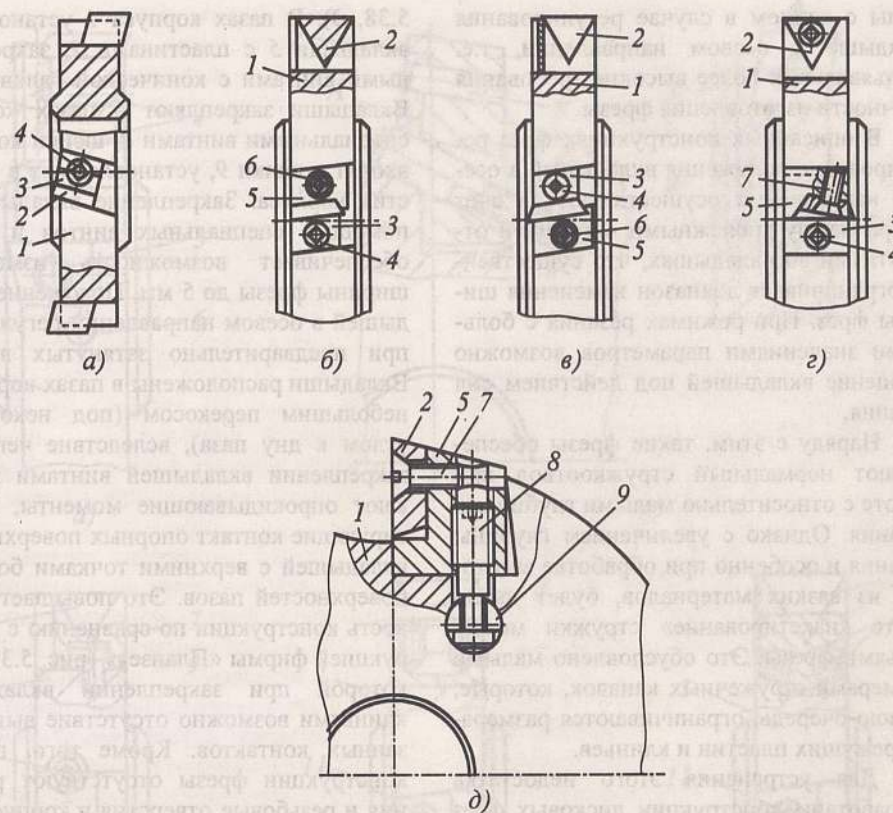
Дисковые фрезы, СМП которых установлены с использованием приспособлений:
